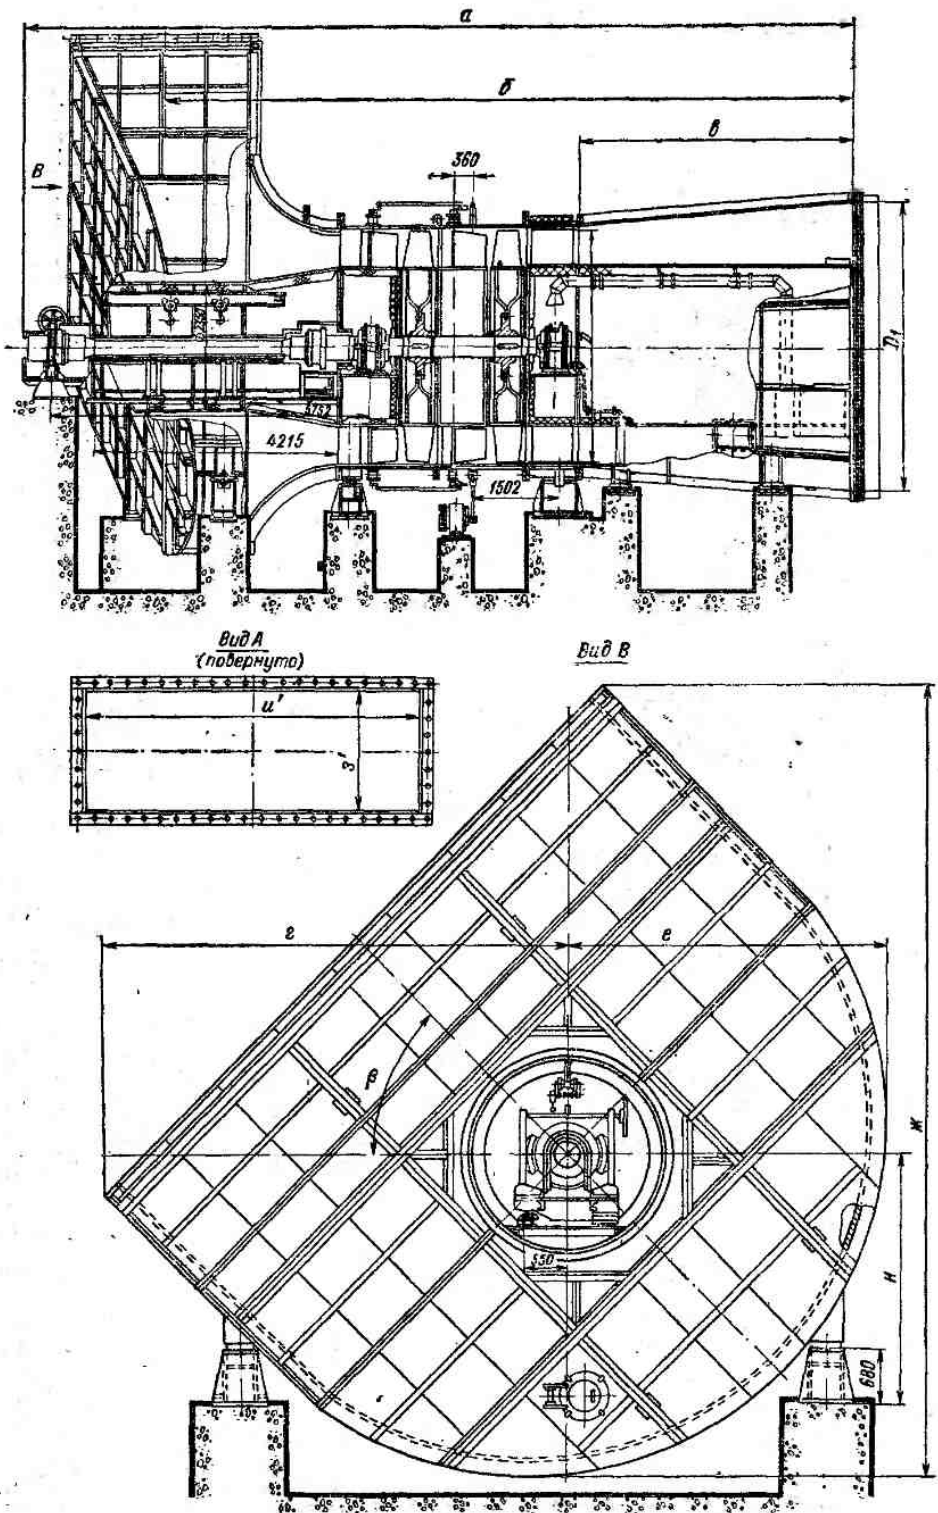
Дымосос осевой двухступенчатый типа К-42Ф (типоразмеры ДОД-41 и ДОД-43)
